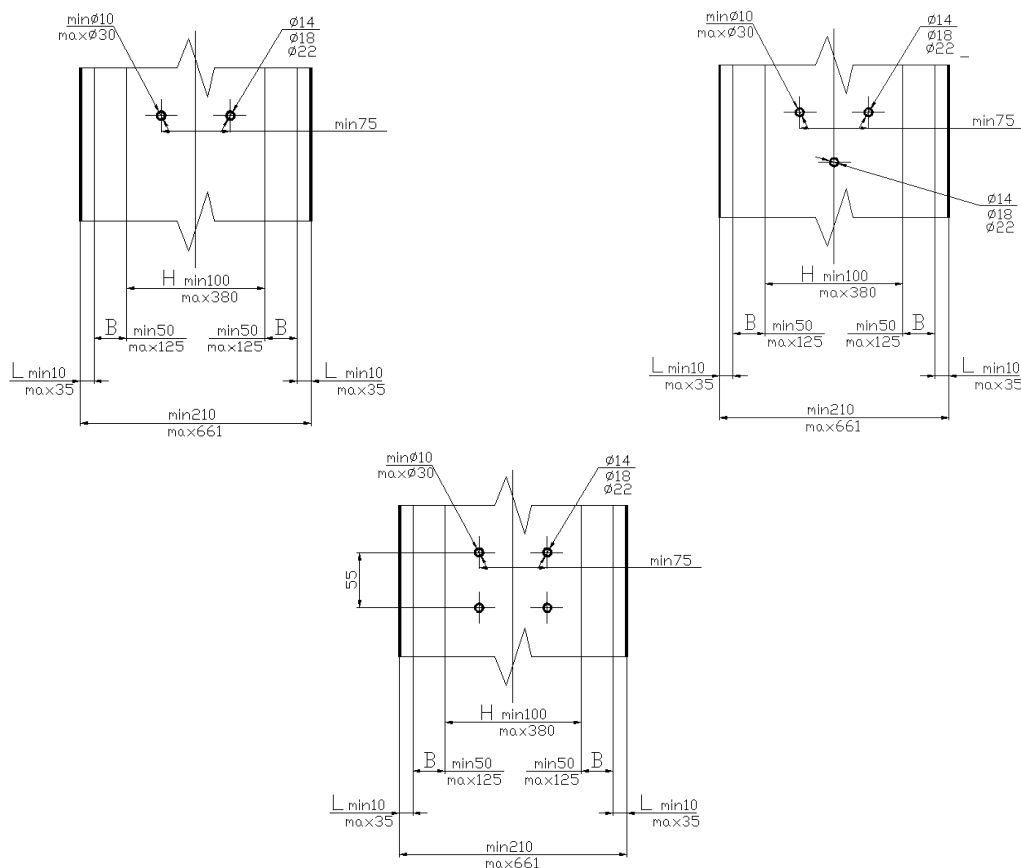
Схемы расположения отверстий в исходной заготовке профиля.
